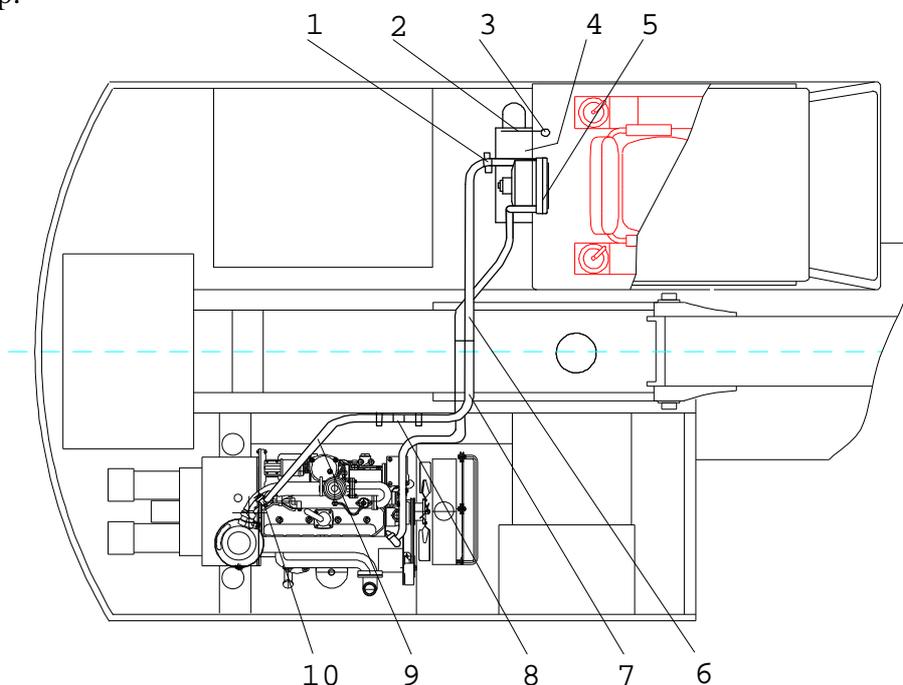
Монтажная схема отопительно-вентиляционной установки
